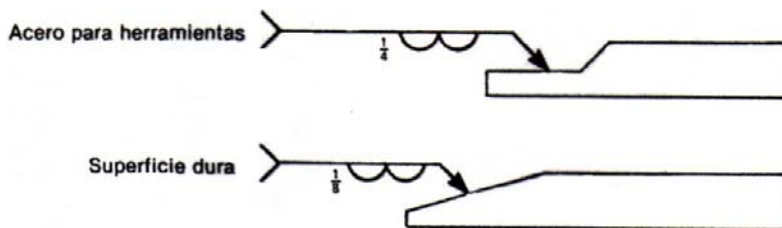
Símbolos de soldadura en los que se especifica la altura máxima de engruesamiento de una superficie que va a ser recubierta
